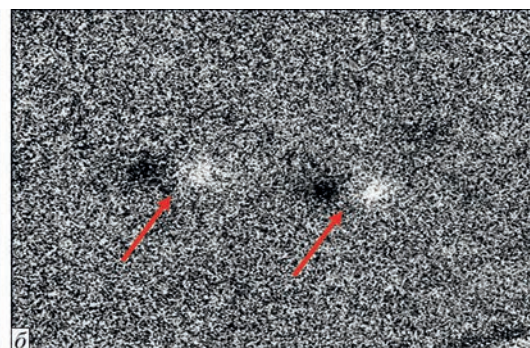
Ширографічний контроль досліджуваної ділянки зварного шва алюмінієвого зразка: загальний вигляд ділянки з дефектами (а) і типова картина виявлених дефектів діаметром  $d = 0,3$  мм і завглибшки  $L = 0,35$  і  $0,85$  мм (б)
